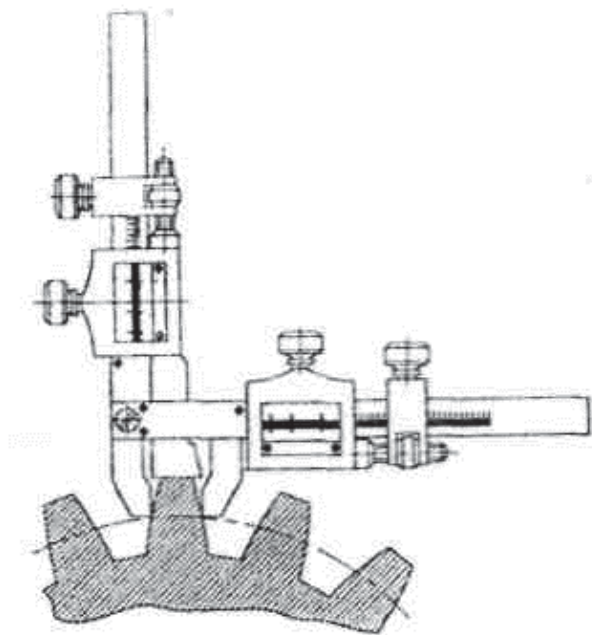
Схема измерения толщины зуба штангензубомером
